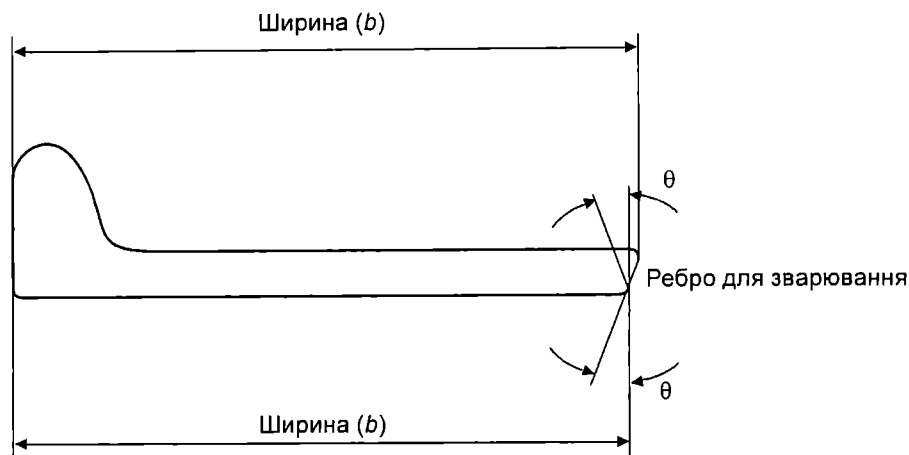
Допуски на косину ребра для зварювання
